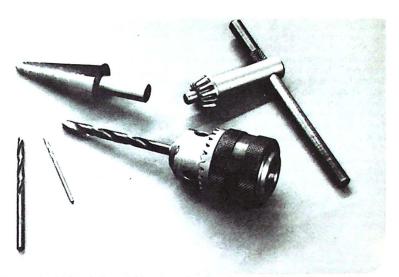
Ein von der Elektrobohrmaschine abgeschraubtes Dreibackenfutter dient beim Kunststoffbohren als Halter zum Bohren mit der Hand.
